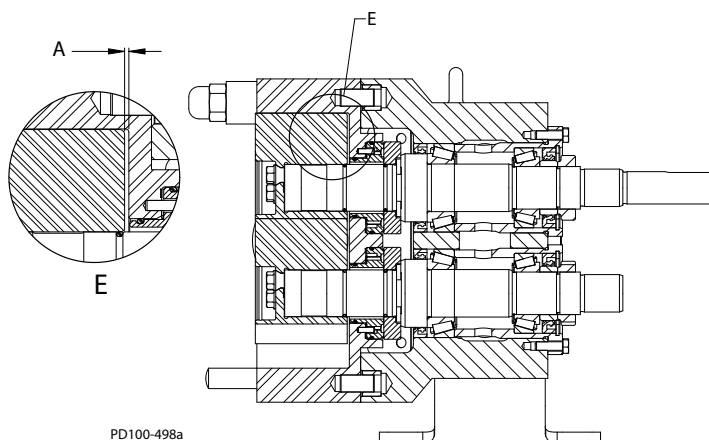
Holgura entre el rotor y el cuerpo de la bomba
